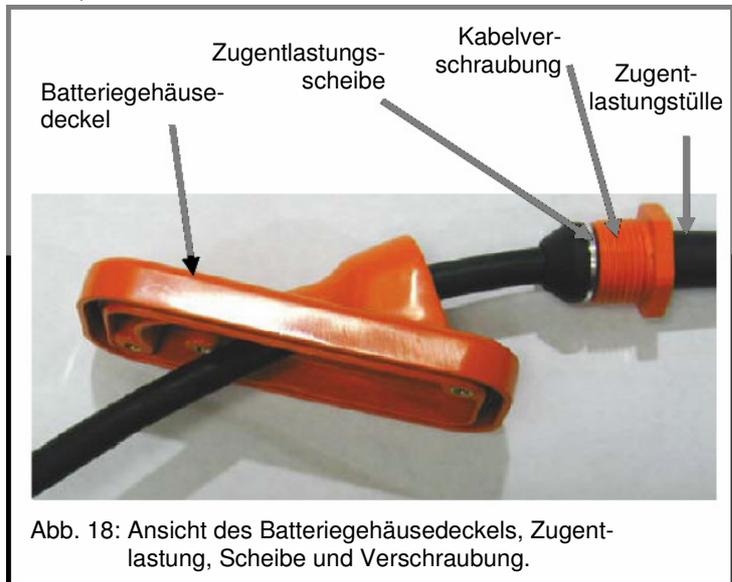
Ansicht des Batteriegehäusedeckels, Zugentlastung, Scheibe und Verschraubung.
